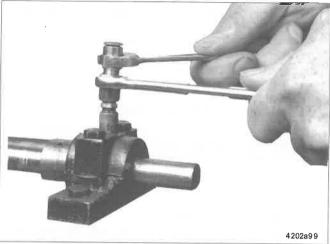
Quicklinc-Steckverschraubung in den Zerk-Lock-Körper einschrauben
